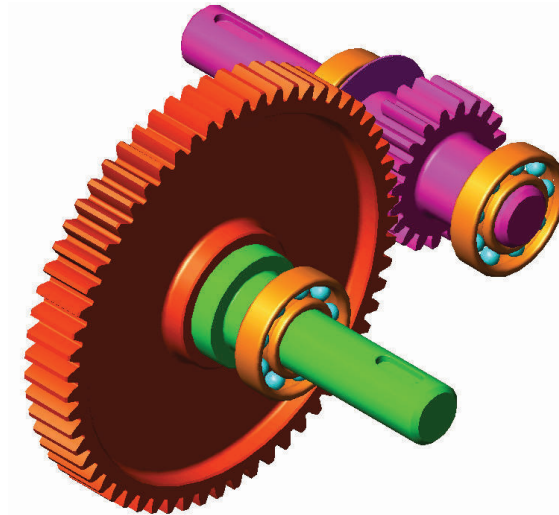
Загальний вигляд тривимірних моделей рухомих частин редуктора
